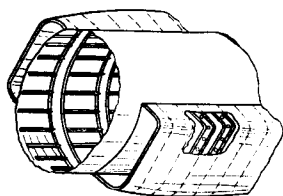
Крепление наружной обшивки канала воздухозаборника.
